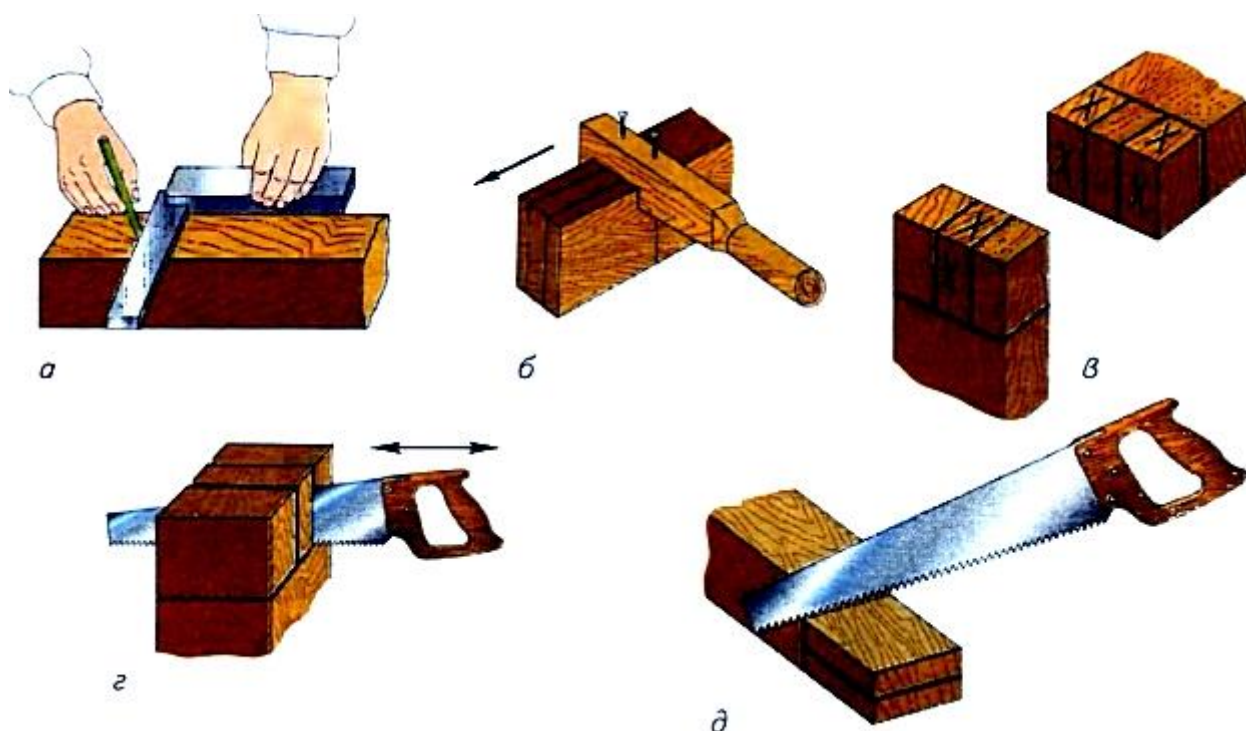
Последовательность изготовления шипового соединения: а — поперечная разметка; б — продольная разметка; в — пометка удаляемых частей заготовки; г — продольное выпиливание шипа и проушины; д — поперечное выпиливание шипов
